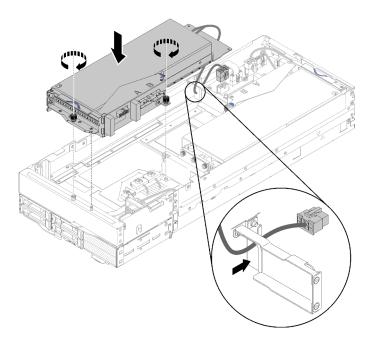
Instalando o conjunto de placa riser frontal no nó de expansão
